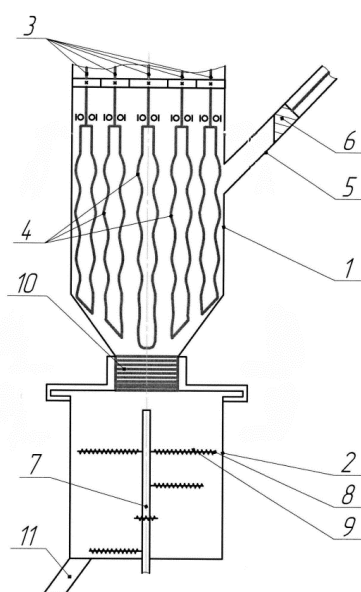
Измельчитель: 1 – загрузочный бункер; 2 – цилиндрическая камера размола; 3 – ротор; 4 – элементы измельчителя с гладкой поверхностью; 5 – загрузитель; 6 – поршень; 7 – ротор; 8 – элементы измельчителя с режущими кромками; 9 – рельеф в виде плотноразмещенных пирамид; 10 – эластичный патрубков; 11 – отводной патрубков
